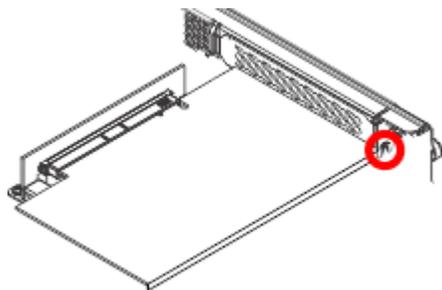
Schraube an der Adapterkassettenhalter wieder anbringen
